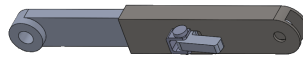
Glissière de réglage de la roue de friction intermédiaire
